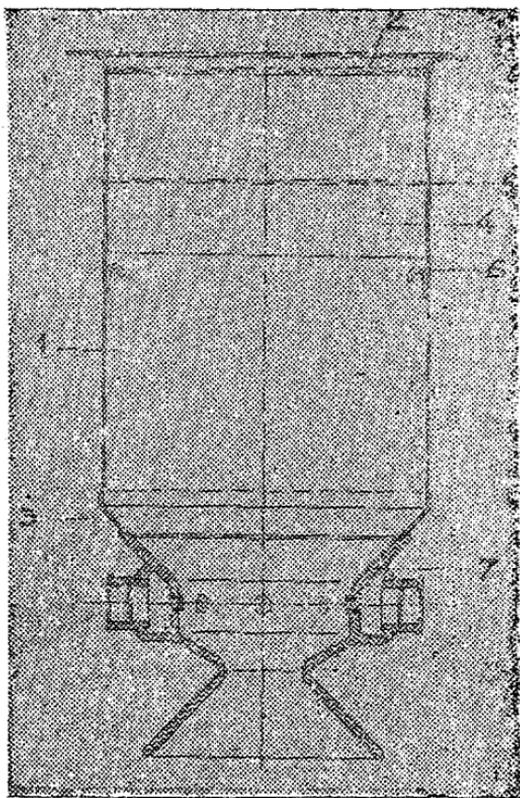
Бункер газогенератора в сборе: 1—корпус бункера; 2—фланец бункера; 3—переходный конус бункера; 4—облицовка бункера; 5—отражатель газа; 6—крючки бункера; 7—камера газификации.
